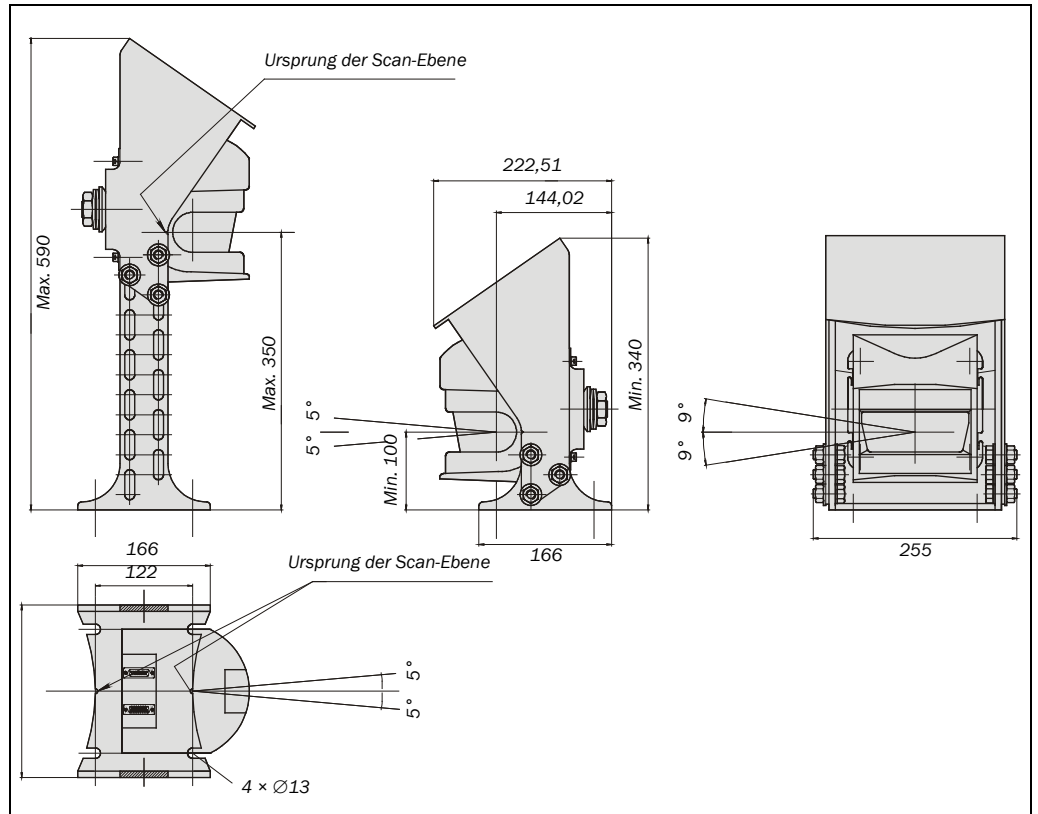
Maßbild Heavy-Duty-Montagehalterung (mm)
